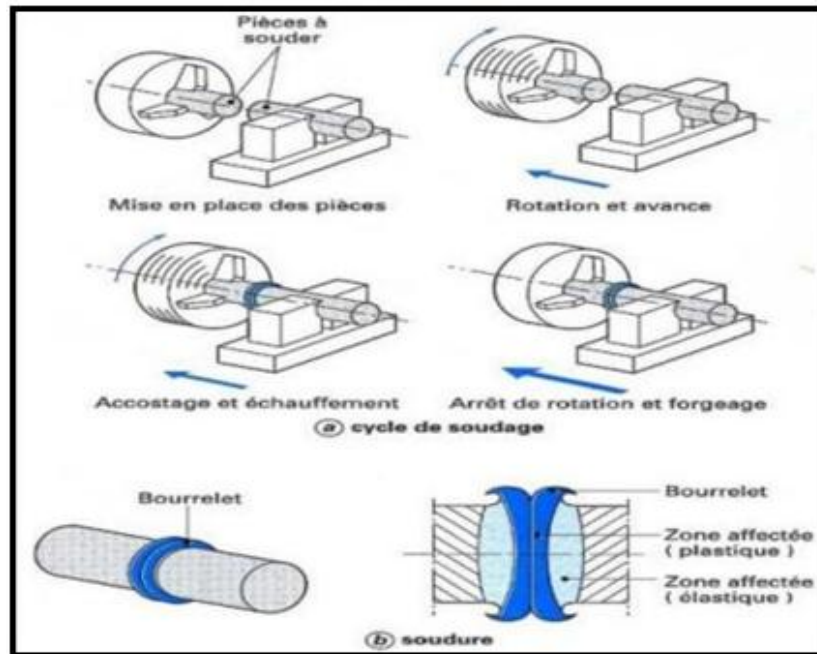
Vue du procédé de soudage rotatif par friction [6].
